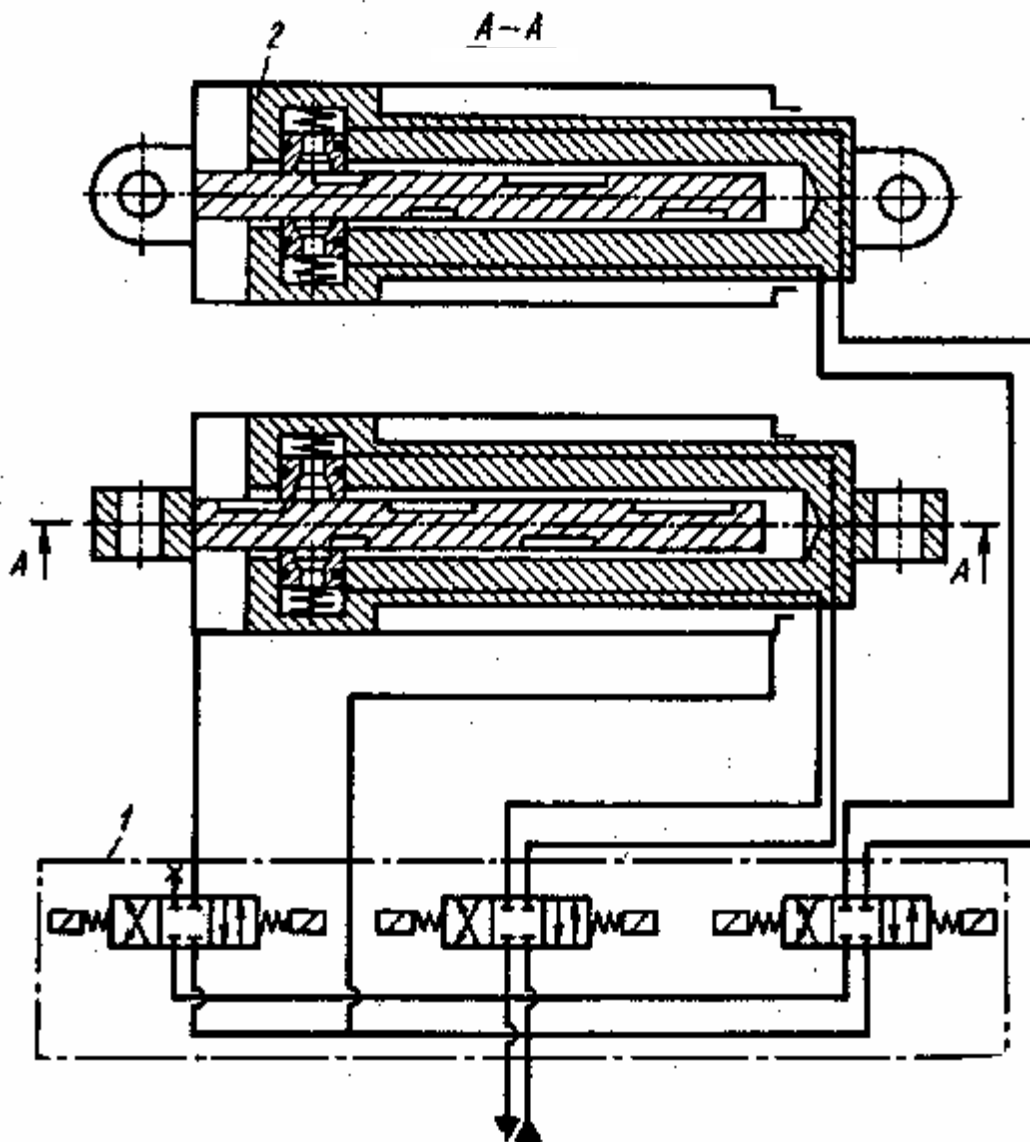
Схема исполнительнй части шагового гидропривода подъемного механизма листоагрузчика автоматической штамповочной линии:
